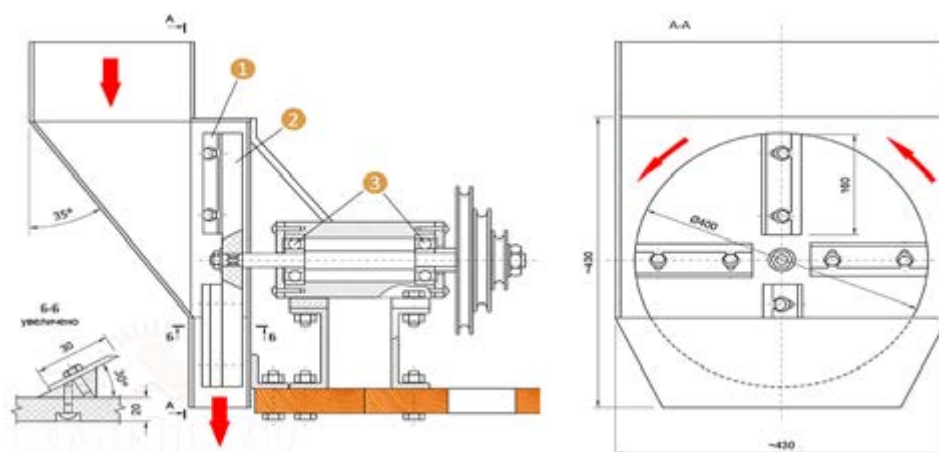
Измельчитель: 1 — ножи; 2 — дисковая фреза; 3 — подшипники
